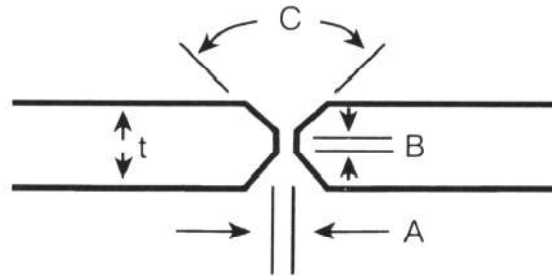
Junta para soldaduras a tope de chapas. [9]
